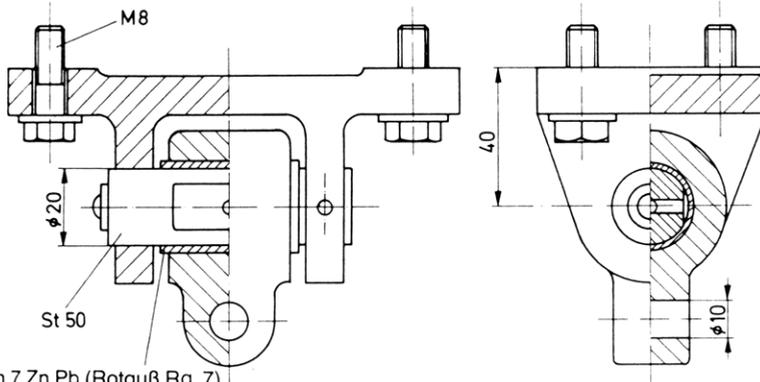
Lagerböcke. Links ausgeprägte Fußflansche, Biegung wird durch Wanddicke beherrscht (Baujahr 1920); rechts zweckmäßige Gestalt (auch für abhebende Beanspruchung geeignet)
